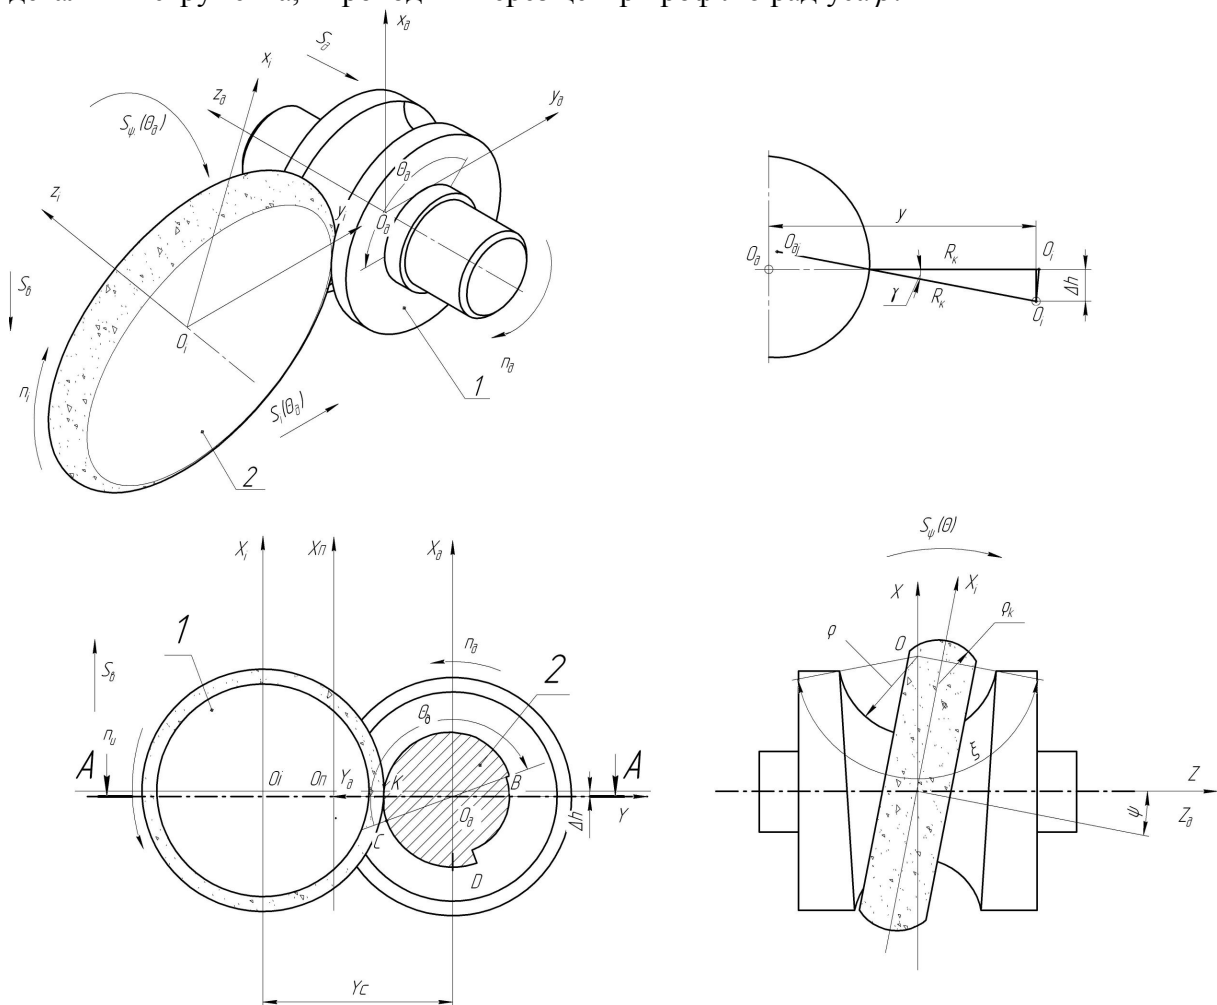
Схема обробки жолоба змінного профілю трубопрокатного валка
